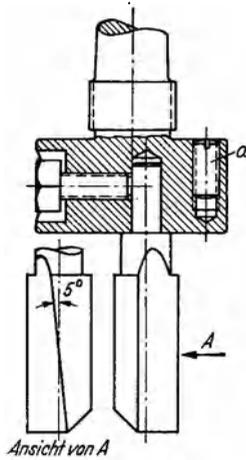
Exzentrisches Spannfutter mit zentralem Fräser. a = Auswuchtschraube.
